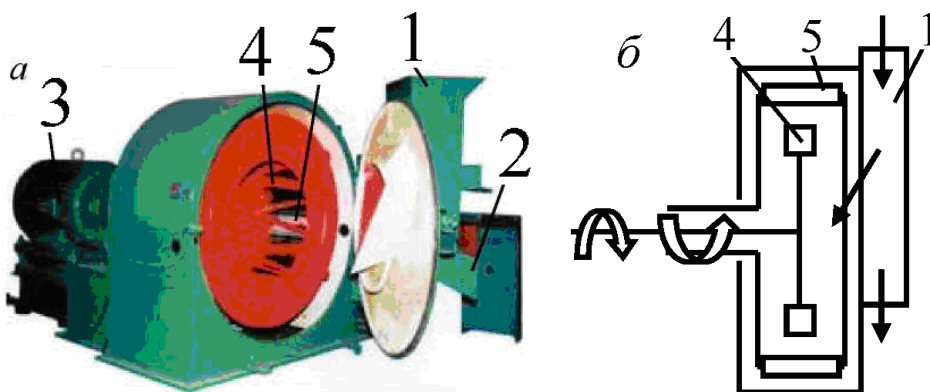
Верстат стружковий ДС-7А: *а* - загальний вигляд;
